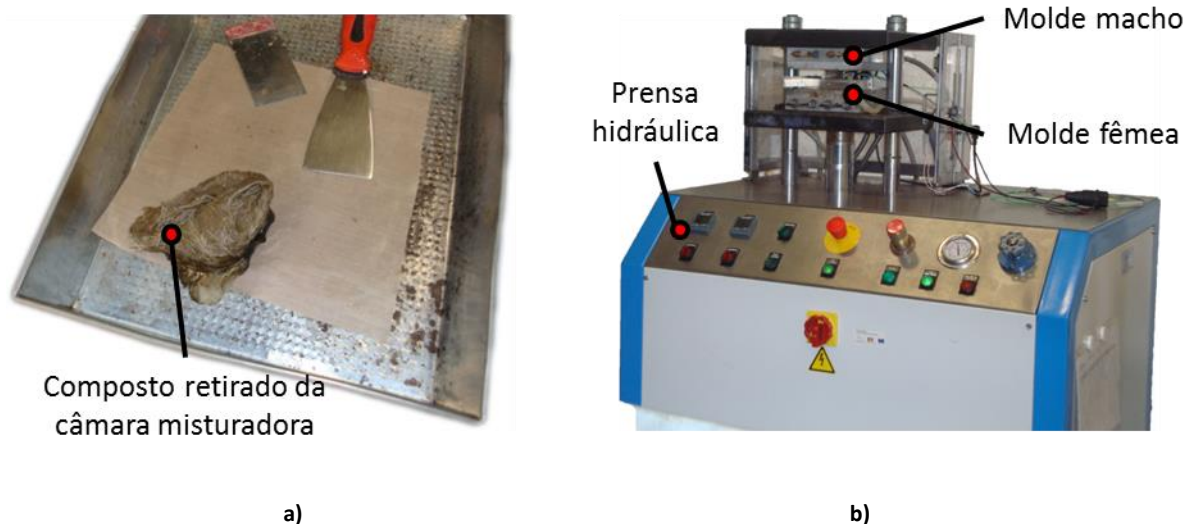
a) Composto de PLA e juta; b) Prensa hidráulica e molde para obtenção de placas
